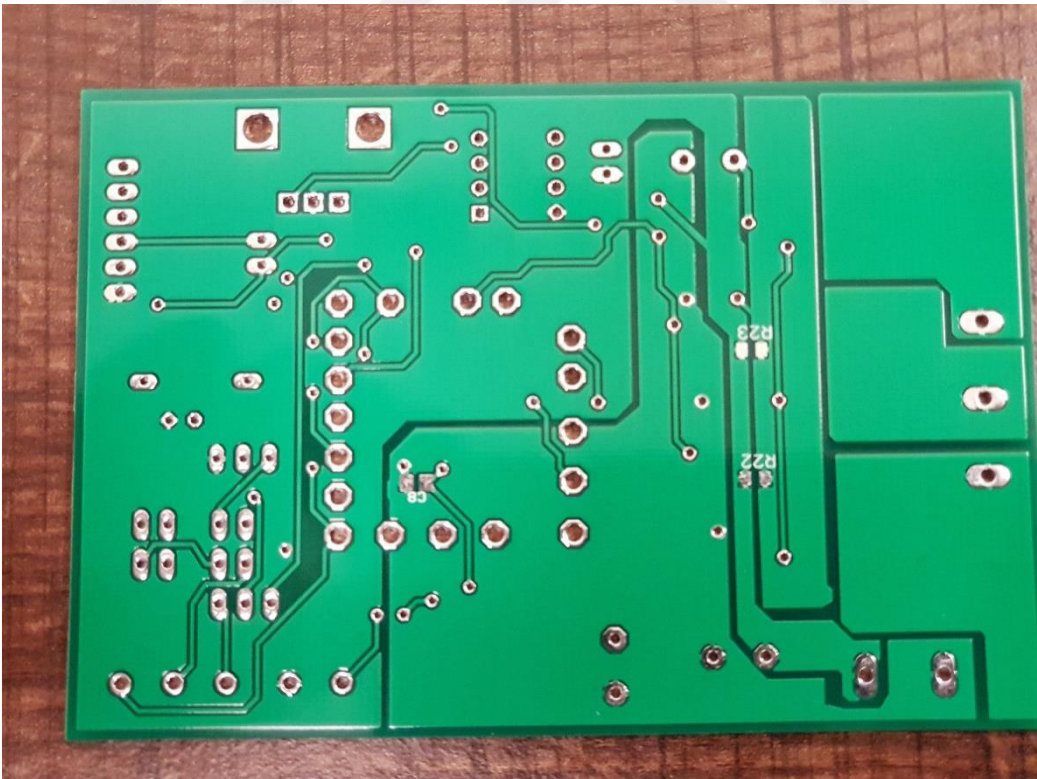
31 BLDC Sürücü PCB Alt Katman Çizimi
